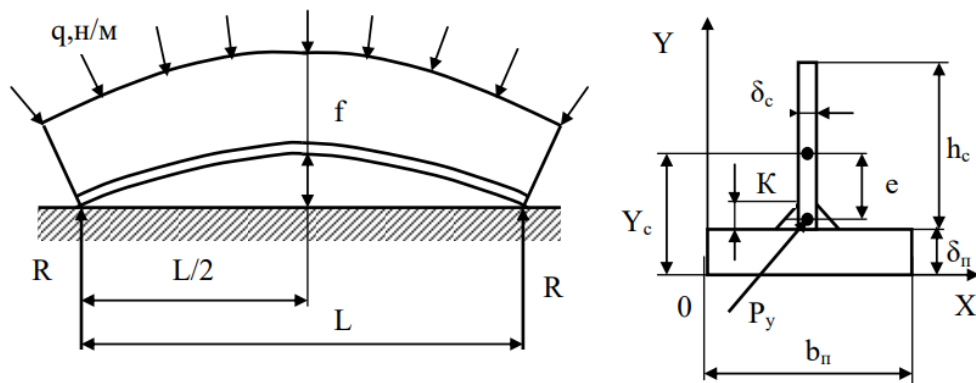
Розрахункова схема притискання заготовок балки рівномірно розподіленими силами
